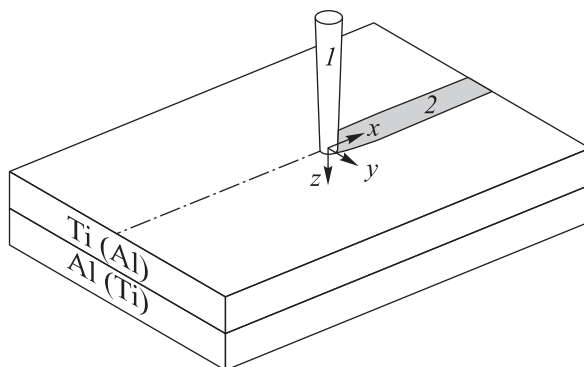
Схема сварки-пайки пластин титана и алюминия:
